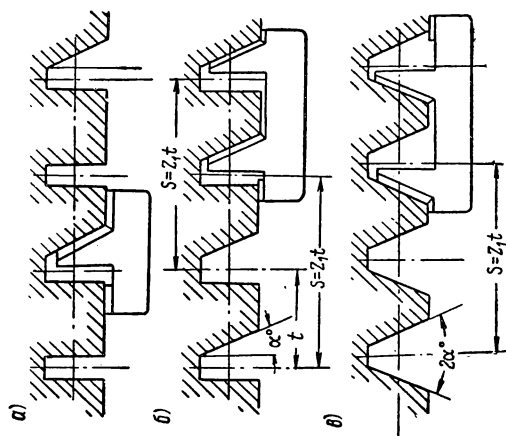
Проверка элементов профиля и шага резьбы с помощью шаблонов.
